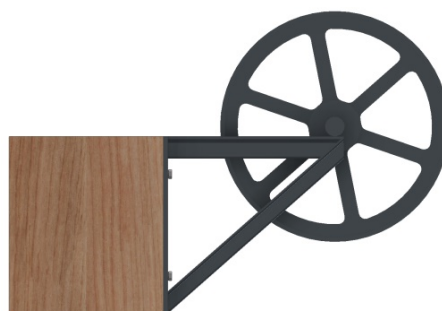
Vista lateral de la viga puente con la polea atornillada.
